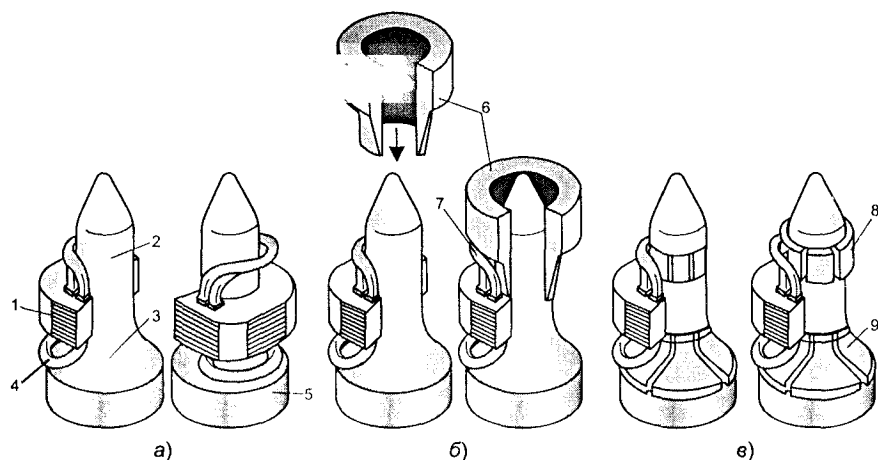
Формовка лобовых частей обмотки статора: а — с помощью одной конусной оправки, б — с помощью двух оправок, в — с помощью оправки с радиально расходящимися сегментами. 1 — статор; 2 — цилиндрическая часть оправки; 3 — коническая часть оправки; 4 и 7 — лобовые части обмотки; 5 — основание оправки; 6 — вторая съемная оправка; 8 и 9 — радиально расходящиеся сегменты
